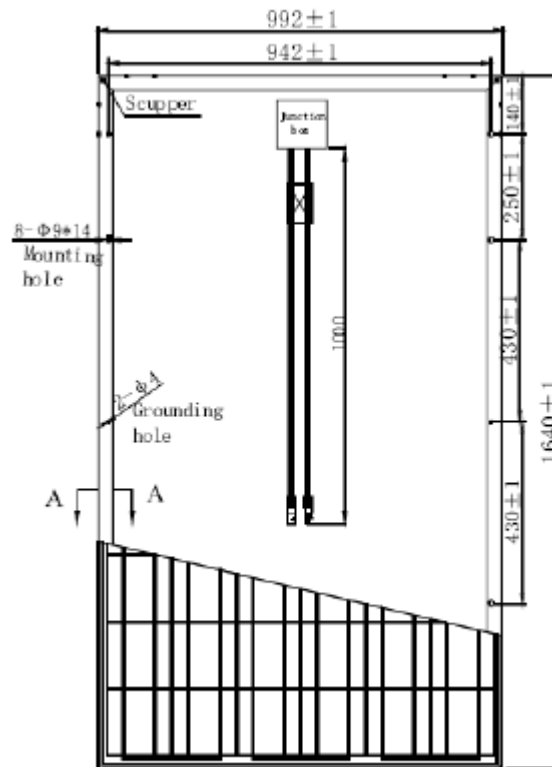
Dimensões do módulo fotovoltaico de 240W (BYD)
